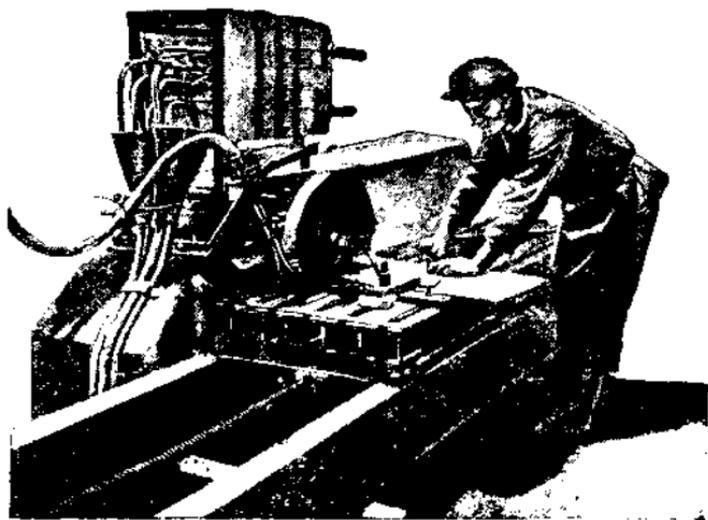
Укрепление каменной доски на тележке фрезерного станка с механической подачей
